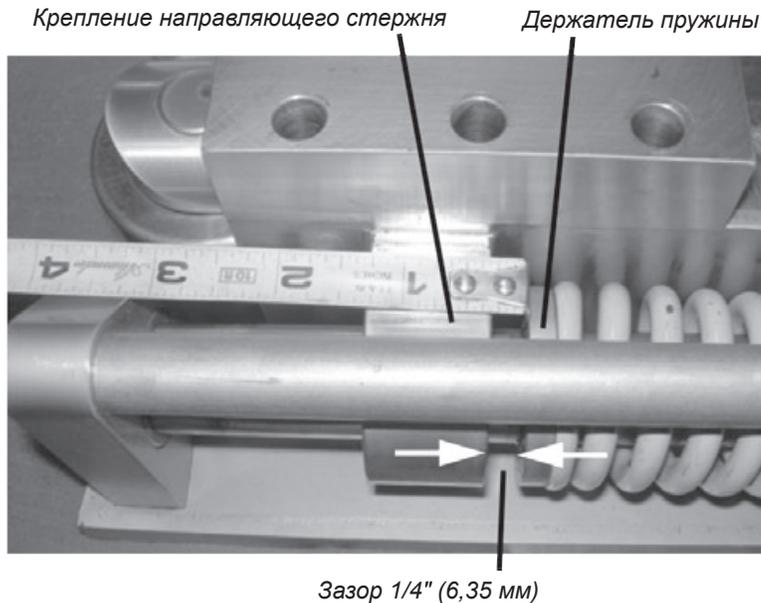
Выставьте суппорт для получения зазора 1/4" (6,35 мм) между креплением направляющего стержня и держателем пружины.
